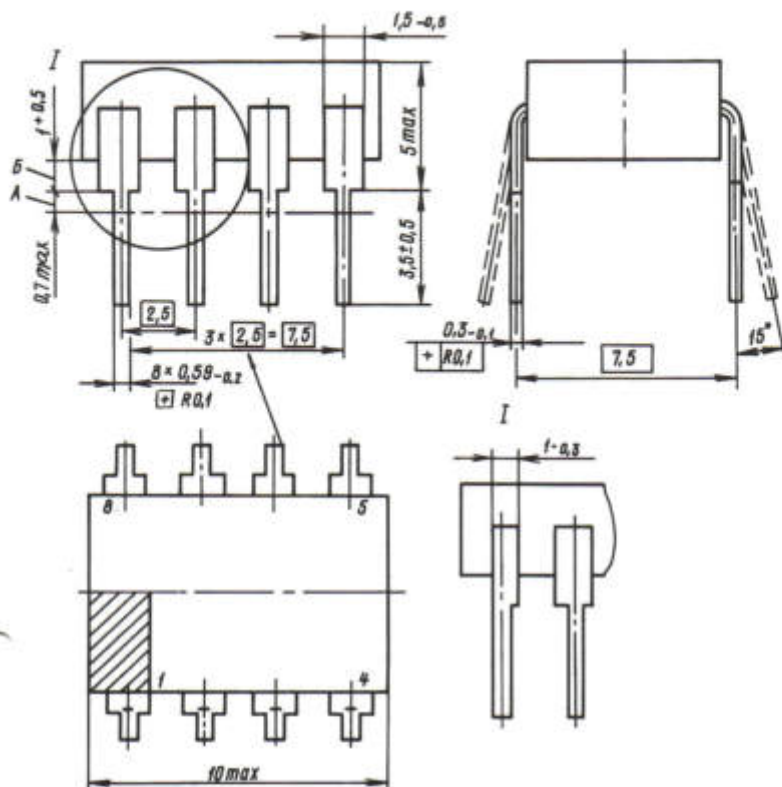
Габаритный чертеж корпуса 2101.8-1 микросхем серии KP544
